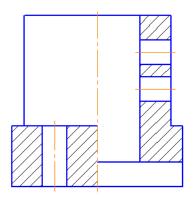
Разрез Б-Б на чертеже детали
